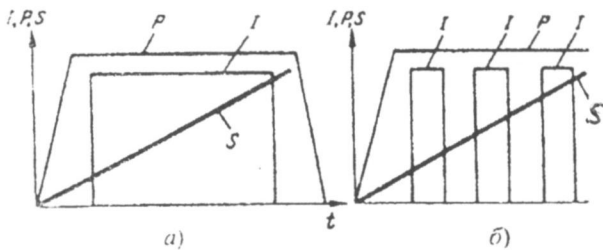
Циклограммы шовной сварки: а – непрерывная сварка; б – прерывистая сварка;
